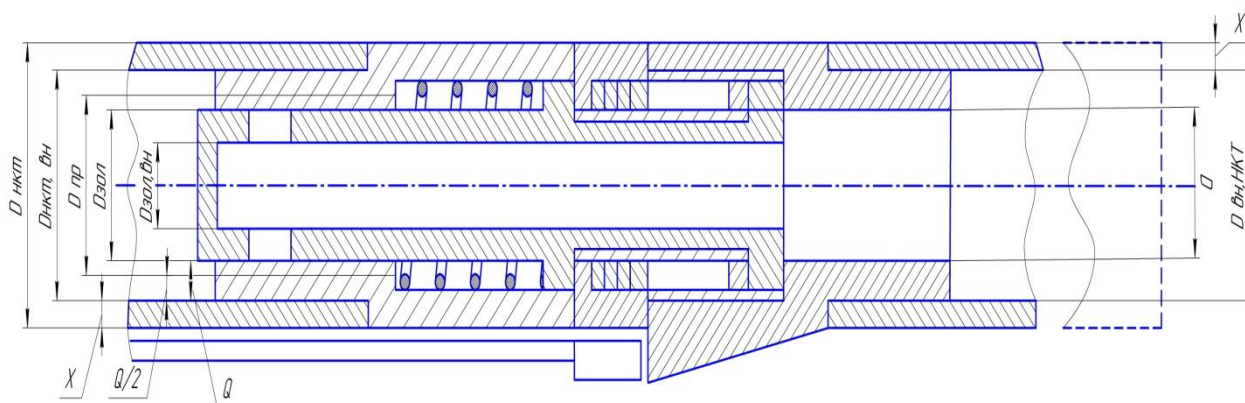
Фрагмент чертежа обратного клапана с электромагнитным приводом
